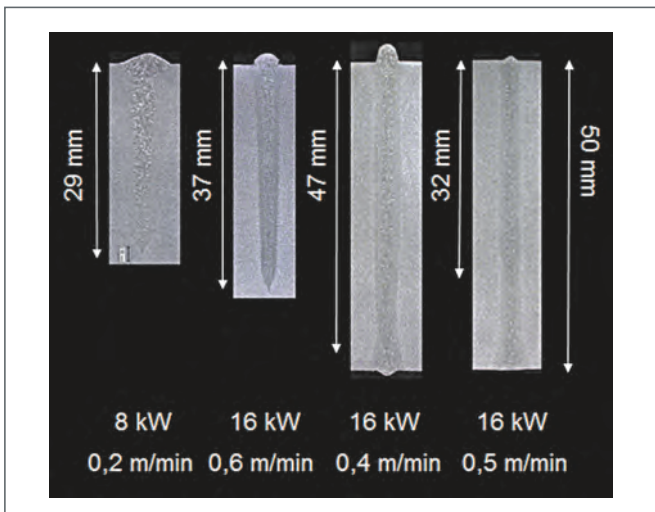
Querschliffe Einschweißungen (links) und Verbindungsschweißungen (rechts), MoVak-LBW, 50 hPa
